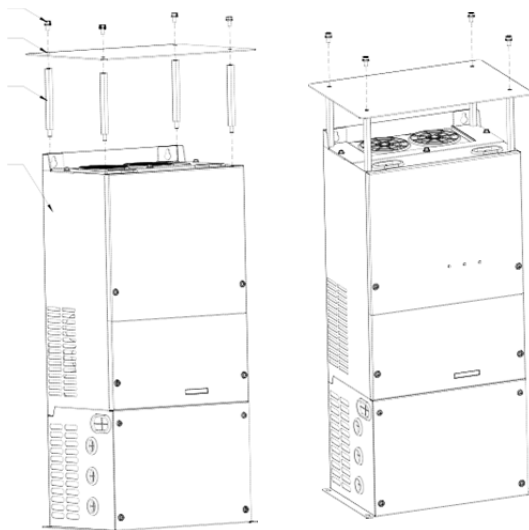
Схема установки каплезащищенной верхней крышки
